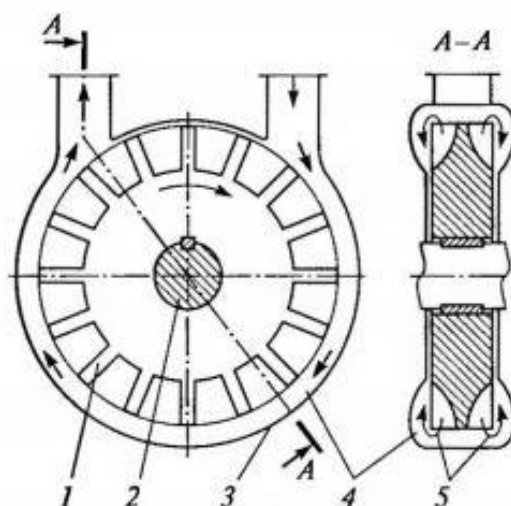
Конструктивная схема вихревого насоса: 1 - рабочее колесо; 2 - вал; 3 - корпус; 4 - концентрический канал; 5 - вихри.
